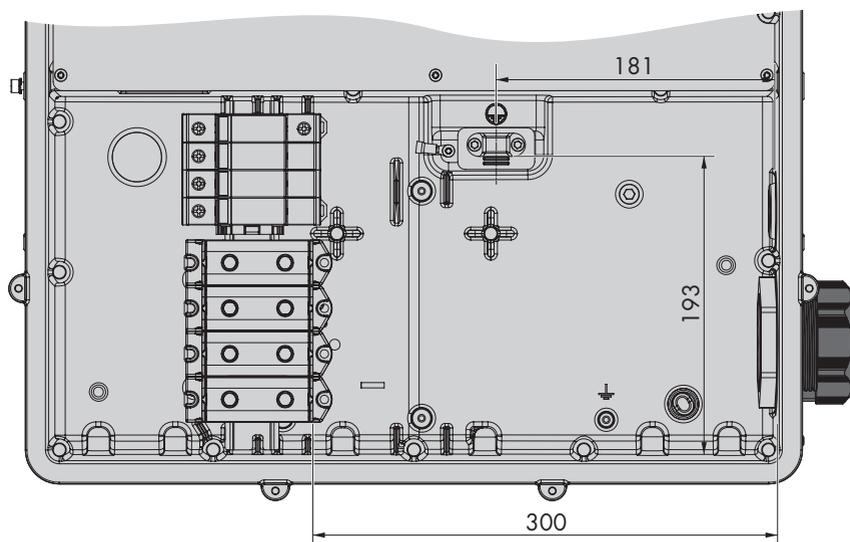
Vista interior da Connection Unit CA com dimensões para os condutores (dimensões em mm)
